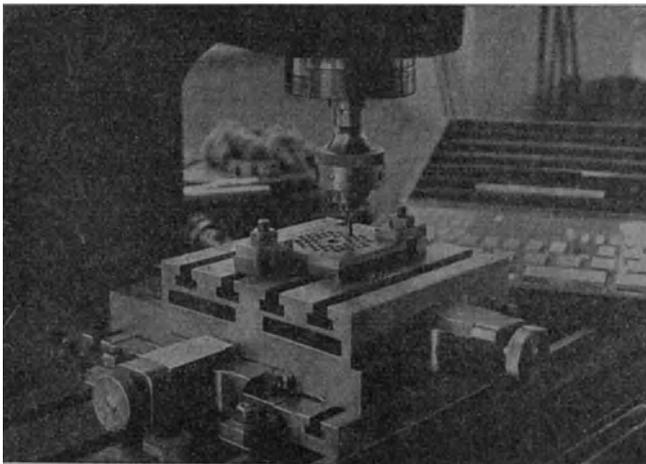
Bohren und Aufreiben einer Schnittplatte mittels Endmaßen auf dem Kreuztisch ohne Anreiben.
